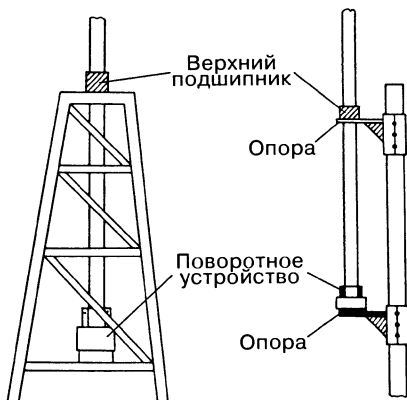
Крепление верхнего подшипника на решетчатой и трубчатой мачтах
